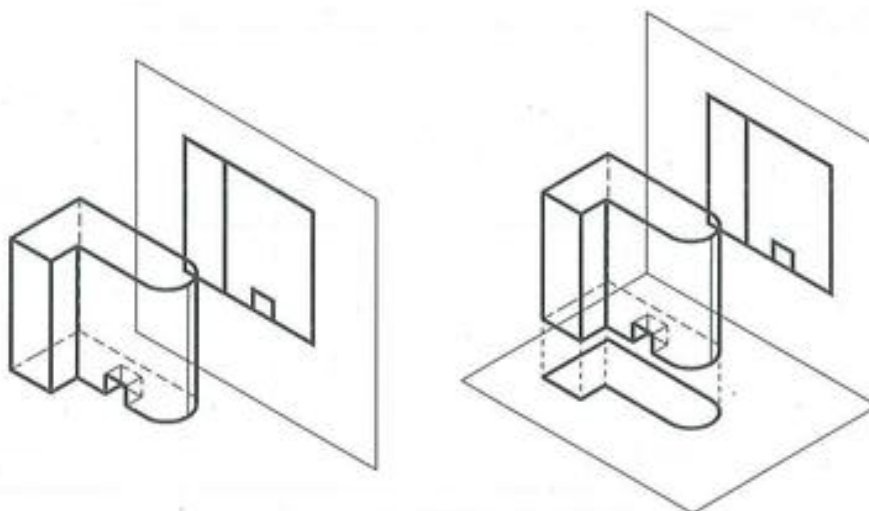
Proyección de la pieza sobre los planos posterior e inferior.
